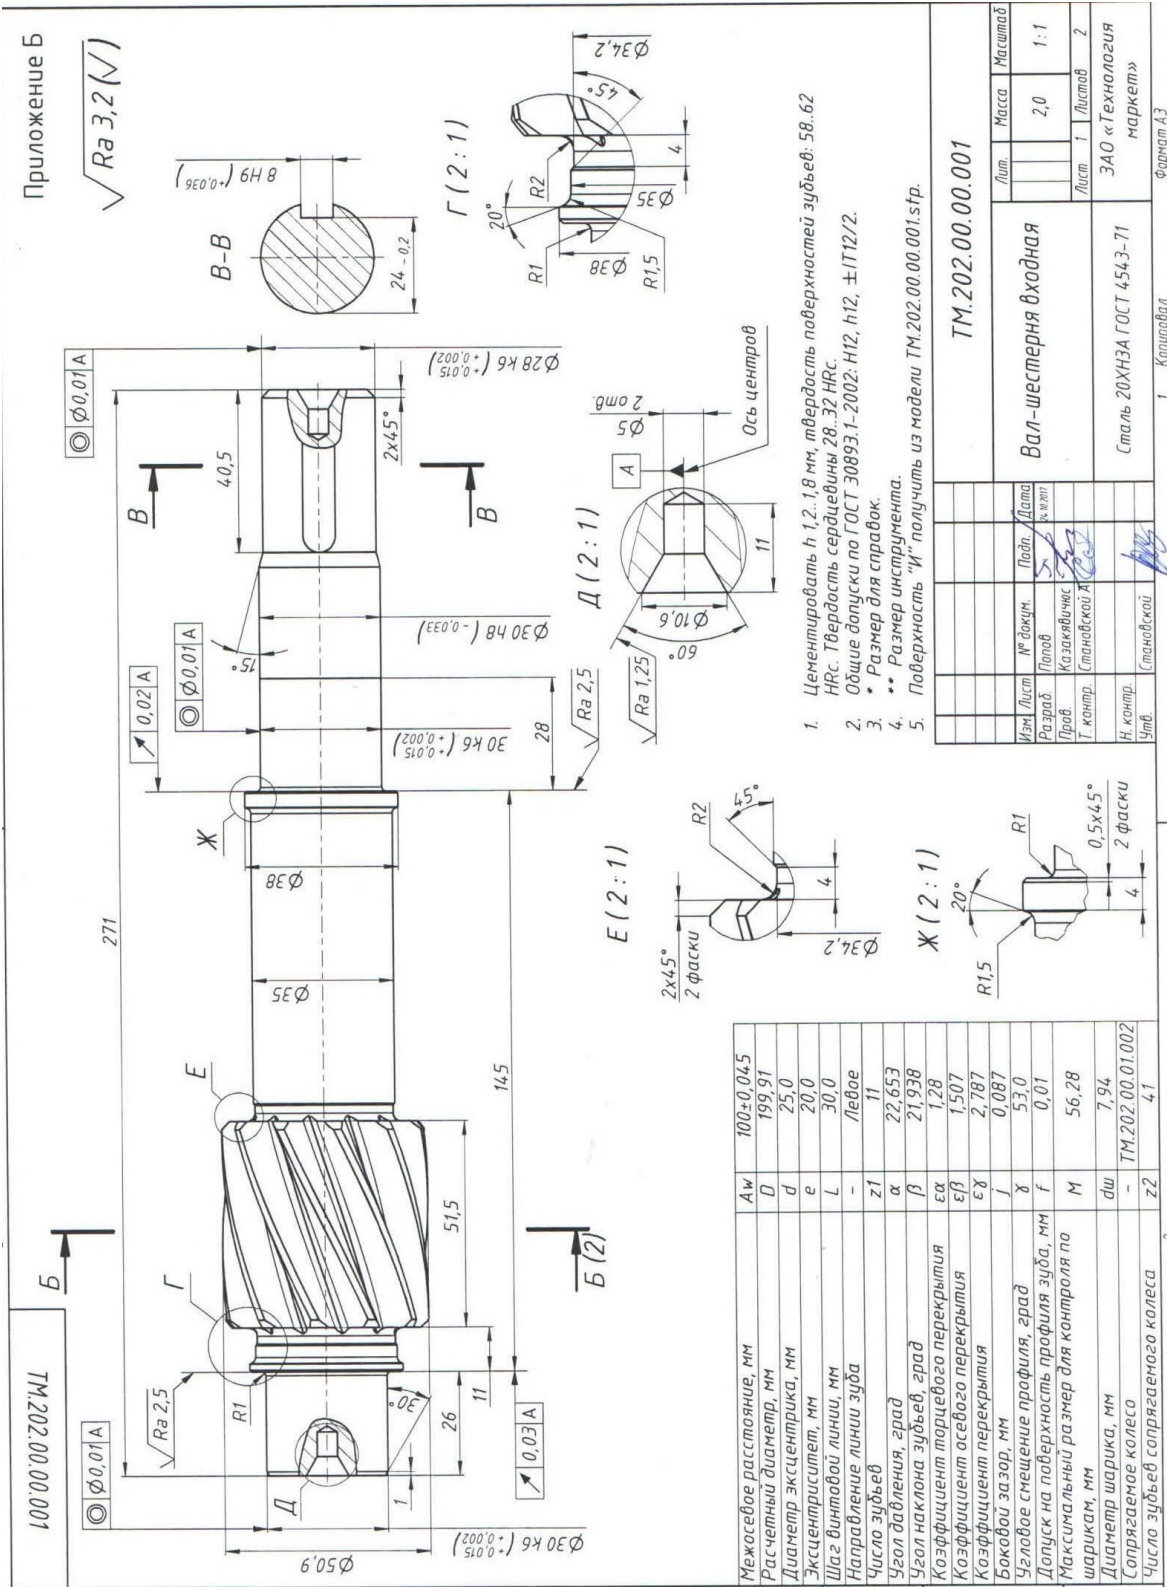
Чертеж вала-шестерни входной редуктора с ЭЦ зубчатым зацеплением
